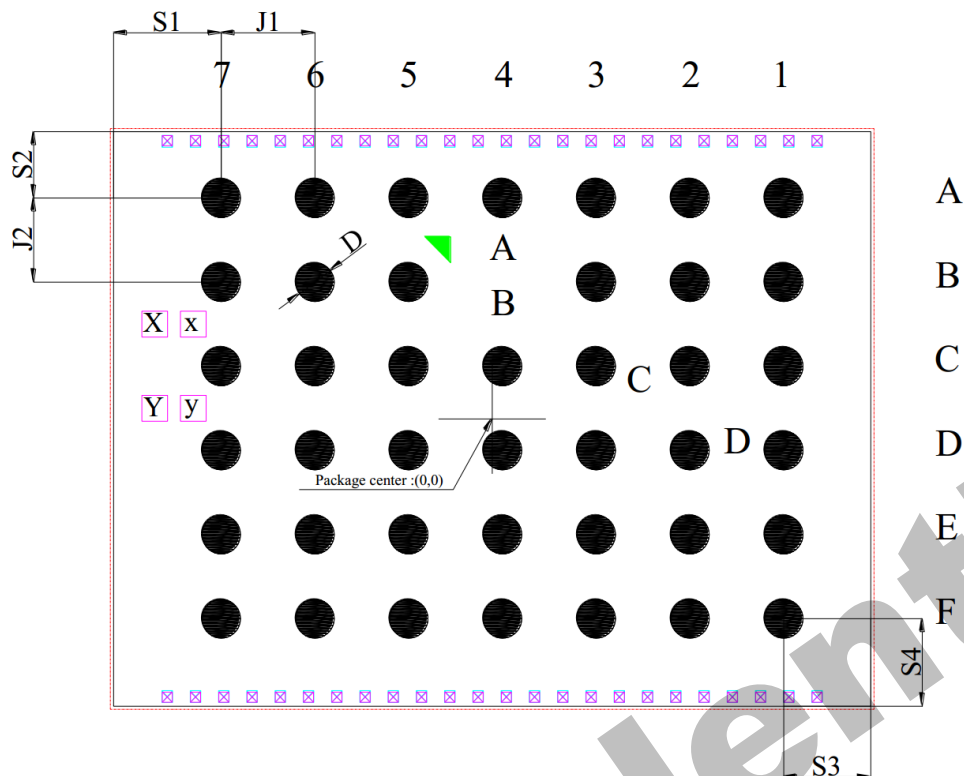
GC4653 封装示意图 (Bottom View BGA Side 单位 μm)
